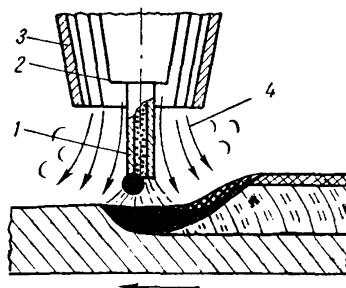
Схема процесса сварки порошковой проволокой в углекислом газе:
